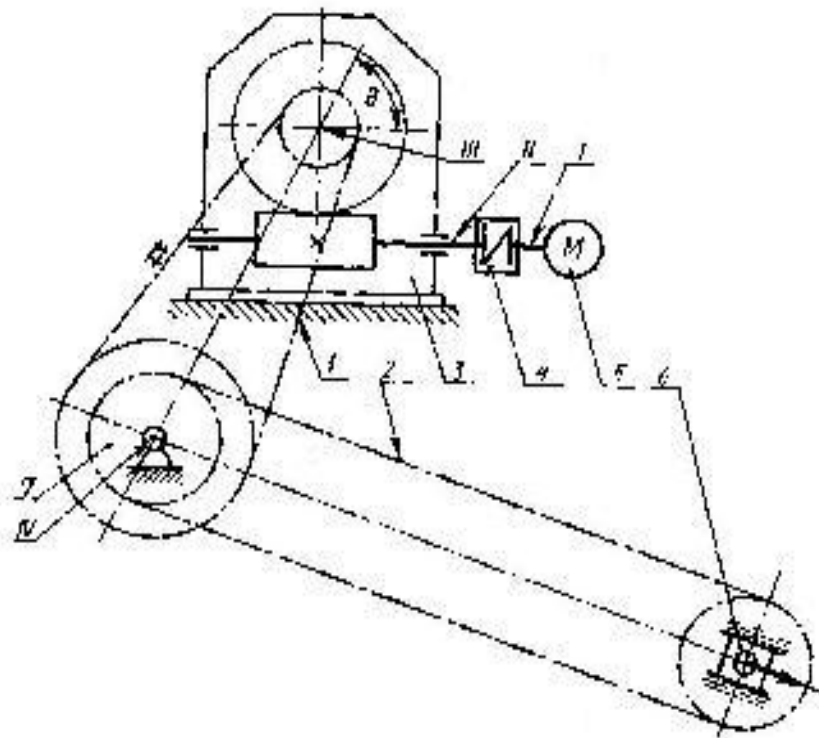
Привод к многоэтажному подъемнику 1 — цепная передача; 2 — грузовая цепь; 3 — червячный редуктор; 4 — упругая втулочно-пальцевая муфта; 5 — двигатель; 6 — натяжное устройство; 7 — звездочка грузовой цепи.
